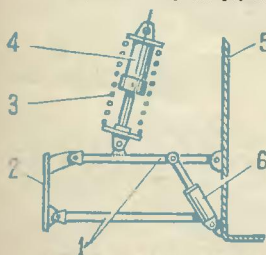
Задний амортизирующий узел: 1 — нижний рычаг подвески; 2 — стойка заднего колеса; 3 — пружина; 4 — пневмоцилиндр; 5 — кузов; 6 — амортизатор.
